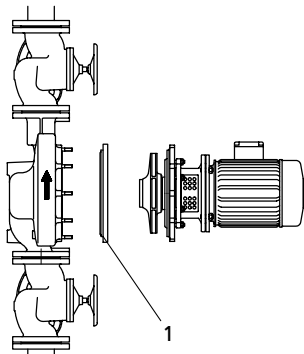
Montaggio orizzontale con flangia cieca (1 = flangia cieca, accessorio)
